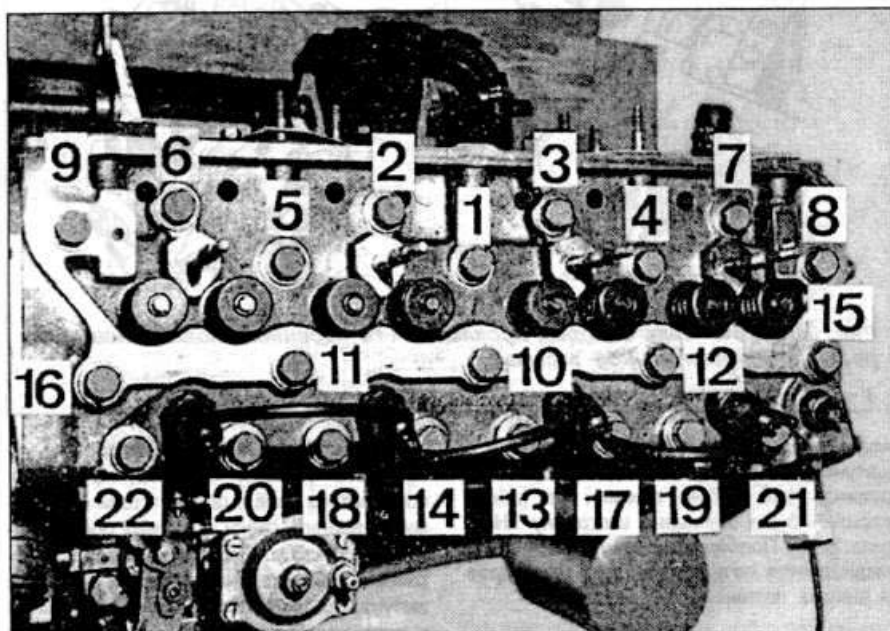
Порядок затяжки болтов крепления головки цилиндров
